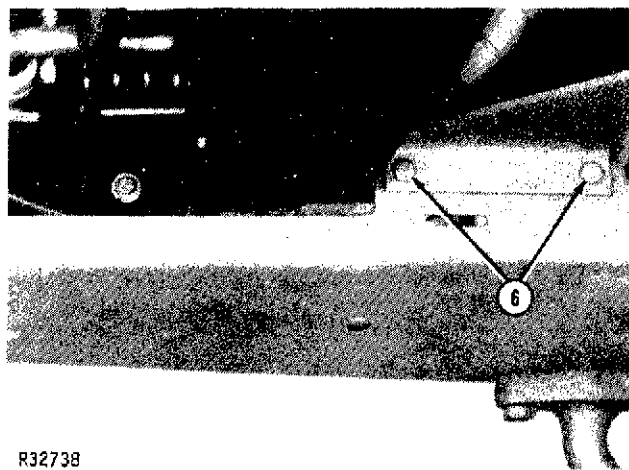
Puntos de Remoción del Lado Izquierdo
